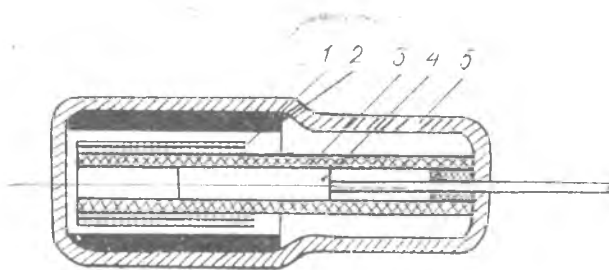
Ферровариометр с подвижным магнитным сердечником: 1 — катушка; 2 — цилиндрический магнитный экран; 3 — каркас; 4 — цилиндрический сердечник; 5 — металлический экран
